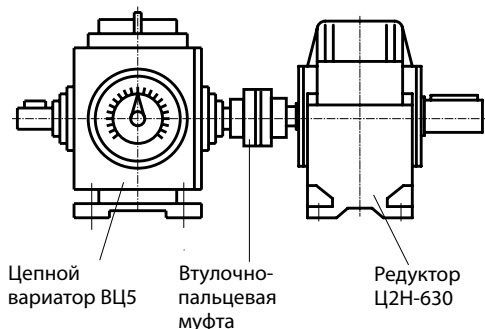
Комбинированная конструкция вариатора цепного с редуктором Ц2Н-630
